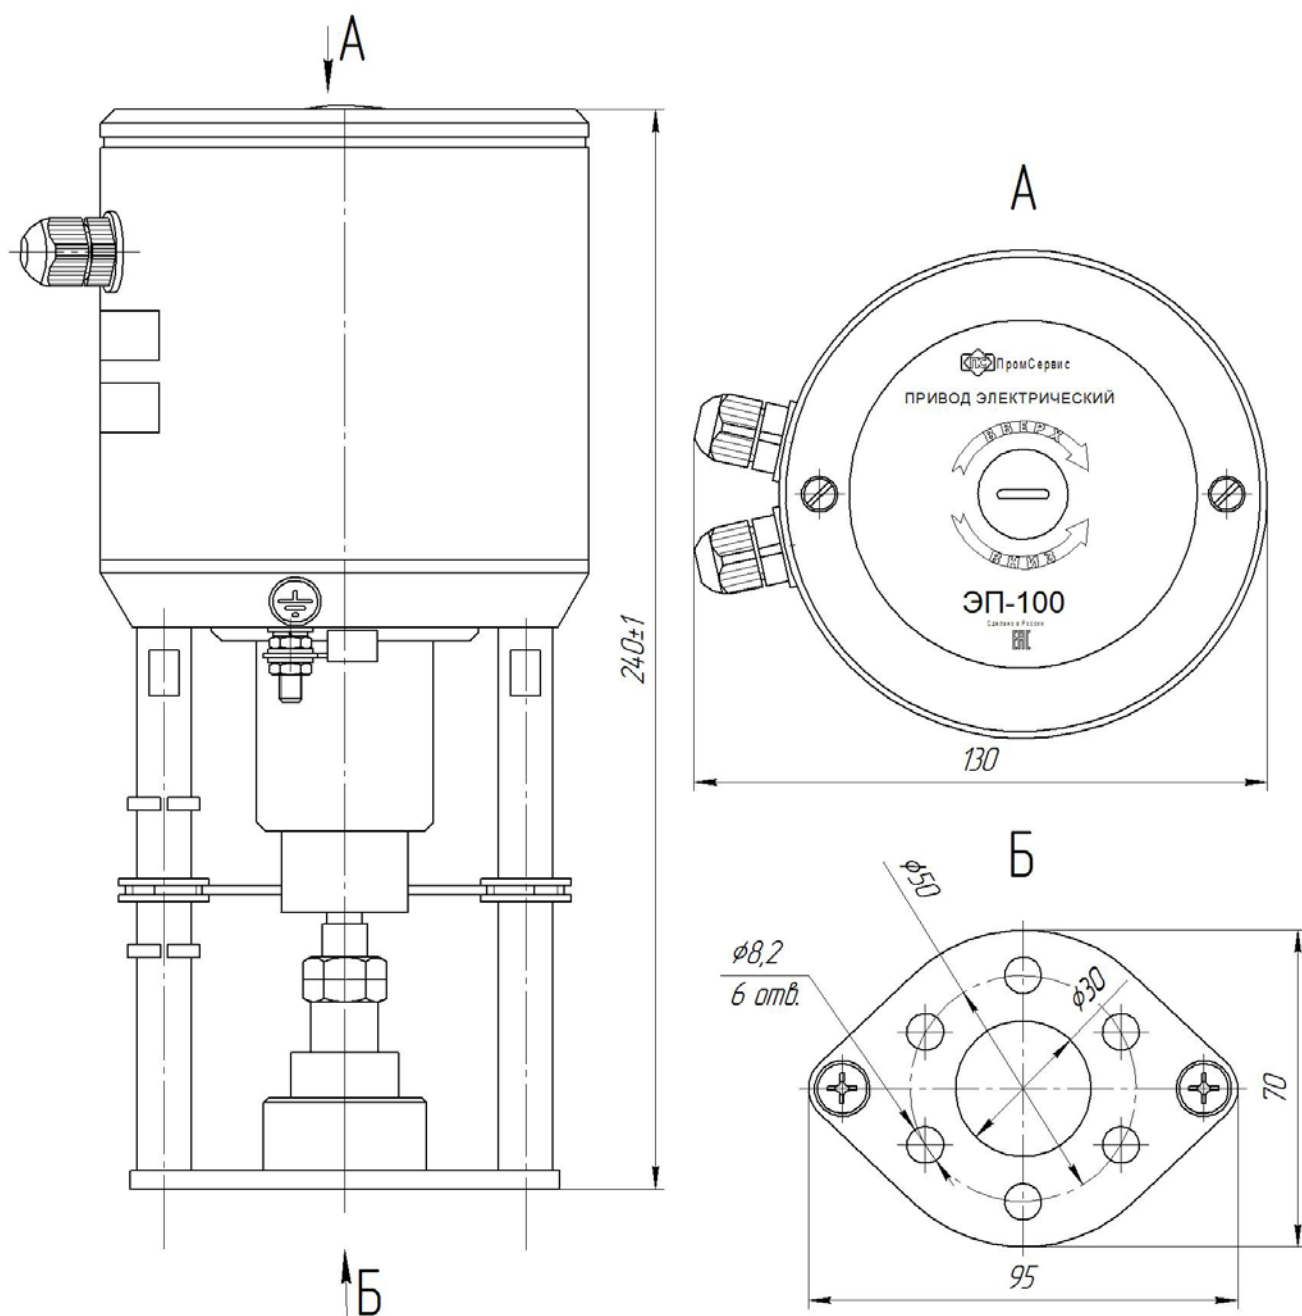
Габаритные и присоединительные размеры привода исполнения ЭП-100-03
